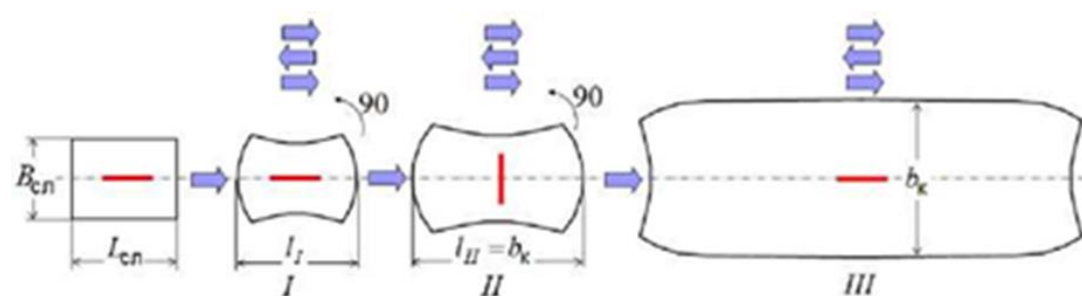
Реверсивная прокатка сляба с разворотом [16]:
